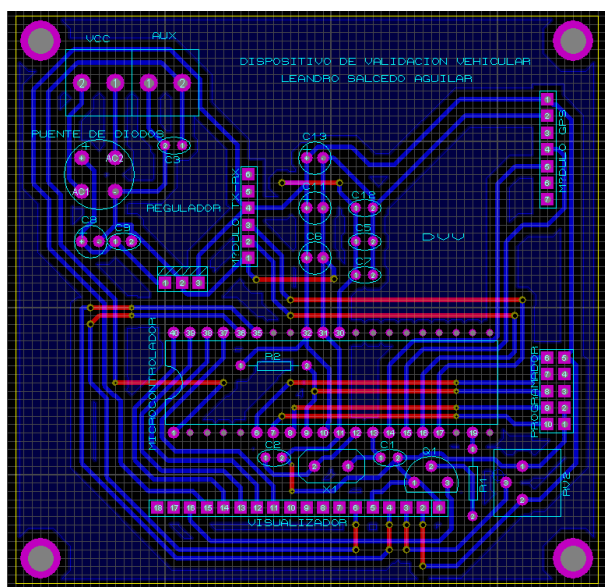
Diseño del PCB del Dispositivo de Validación Vehicular
